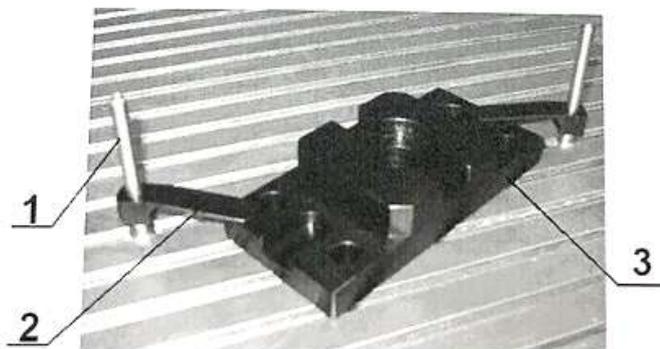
Общий вид закрепления детали на рабочем столе:
